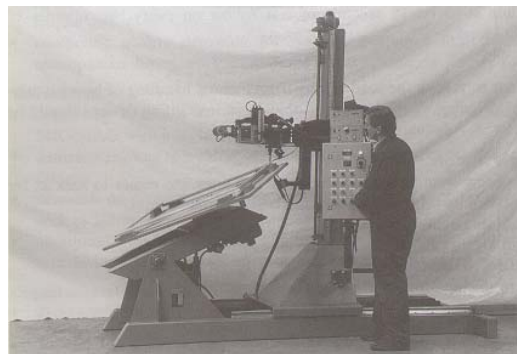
Posto de soldagem do tipo Máquina/Robô (BOEKHOLT, 2000)
